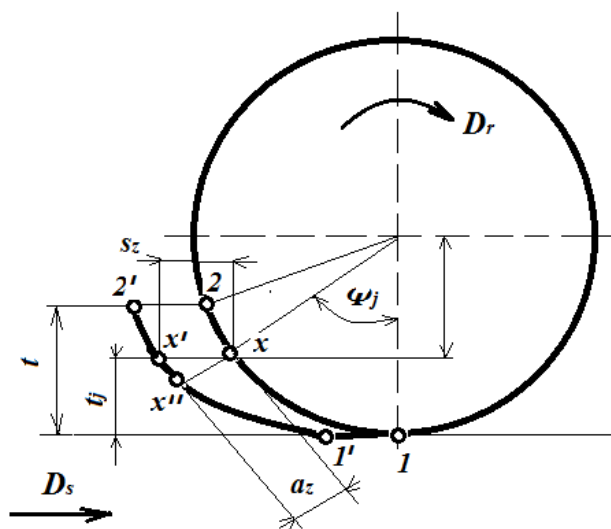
Розрахункова схема для визначення товщини шару, що зрізається зубом фрези
